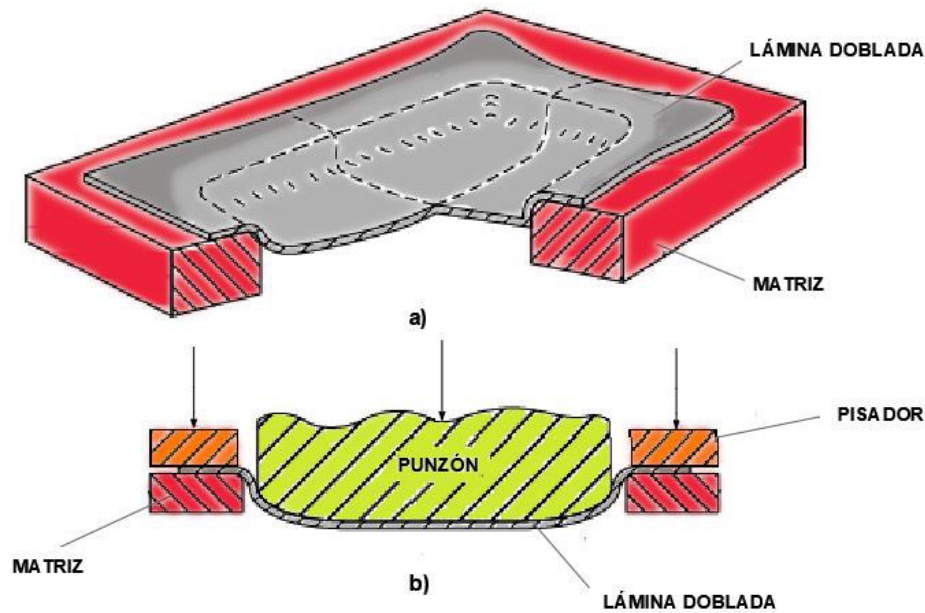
a) Parte típica formada en un troquel de estampado. b) Sección de herramientas en una matriz de extracción que muestra el conjunto de los herramientas [3].
